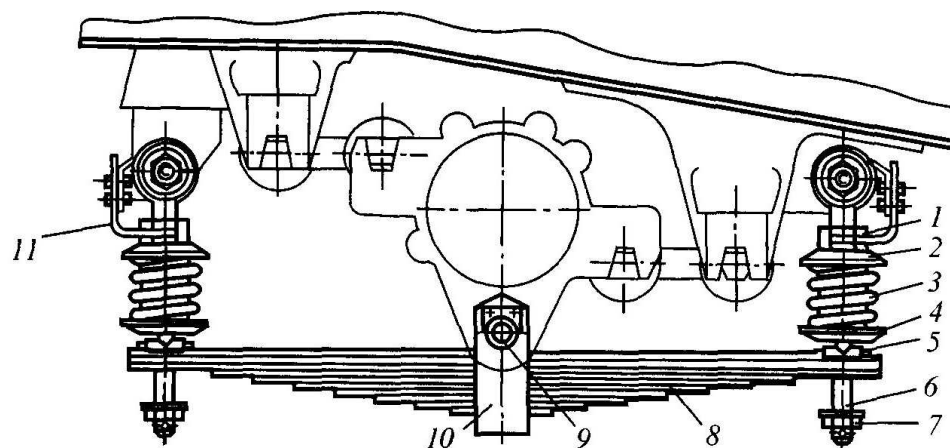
Рессорное подвешивание буксового узла: 1- регулировочная гайка; 2 - верхняя стальная шайба; 3 - цилиндрическая пружина; 4- нижняя стальная шайба; 5 - опора (подкладка); 6- рессорная стойка; 7 - предохранительная гайка с шайбой и шплинтом; 8 - листовая рессора; 9 - валик рессоры; 10 — хомут рессоры; 11 — стопорная планка
